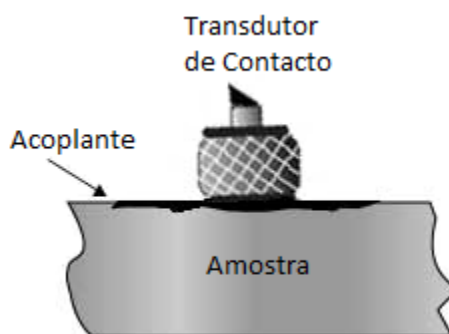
Esquema do acoplante entre as faces do transdutor e da amostra (NDT, n.d.).
